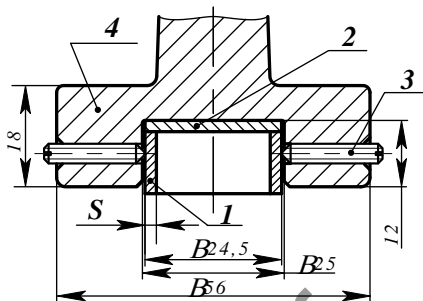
Оправки машины трения, с зажатой в ней парой трения: 1 – образец для пары трения, который изготавливается из материала рабочих валков; 2 – опорная шайба; 3 – шпильки зажатия и центровки; 4 – оправка УМТ; S – толщина стенки образца
